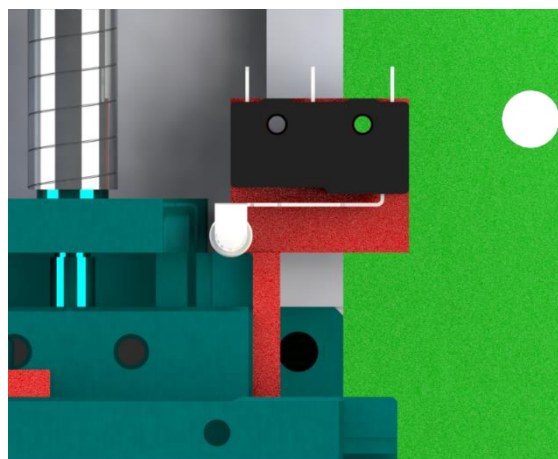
Mínima invasión del micro switch de Motor Y montado al posicionador
